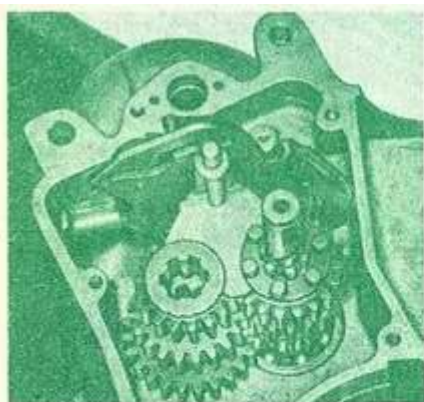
Зубчатое колесо III промежуточного вала, надетое канавкой на верхнюю вилку
